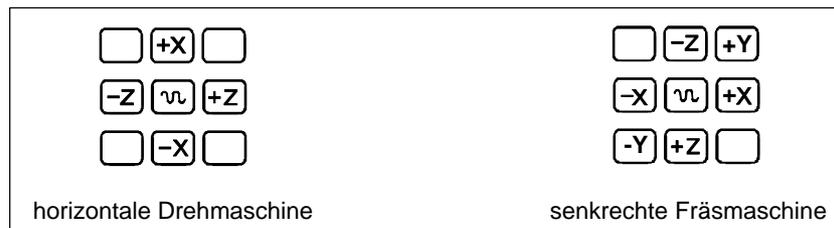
Beispiele für die Belegung des Achstastenfeldes
